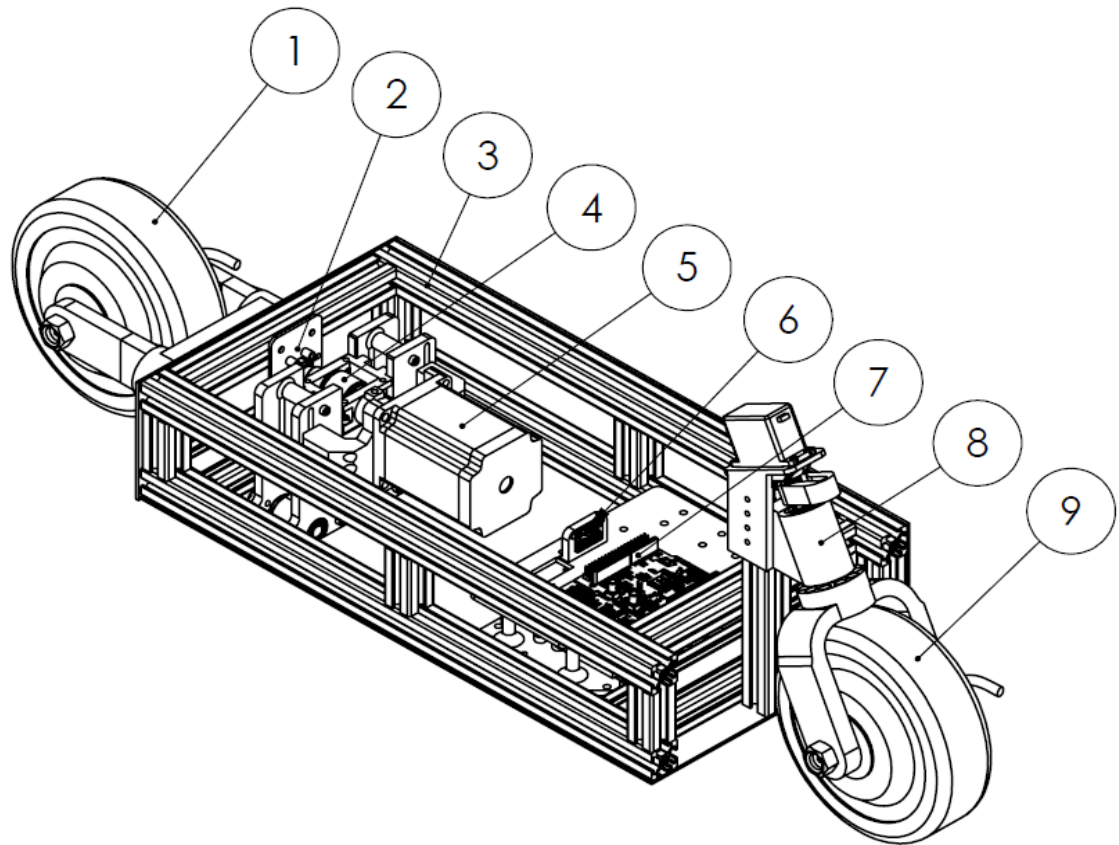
3D-модель пристрою: 1) заднє приводне мотор-колесо; 2) датчик повороту заднього колеса; 3) рама пристрою; 4) механізм балансування; 5) кроковий електродвигун; 6) гіро-акселерометр; 7) плата керування; 8) поворотна стійка з механізмом повороту колеса; 9) переднє приводне мотор-колесо
